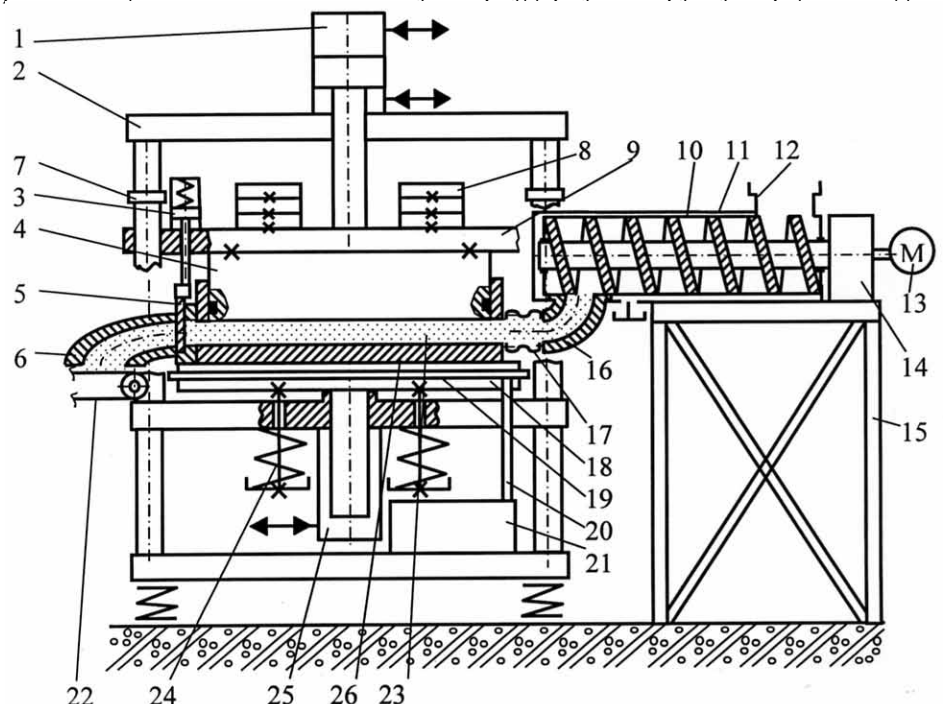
Схема шнекового пресса и вибропресса с ГИП для предварительного обезвоживания твердой фазы отходов
